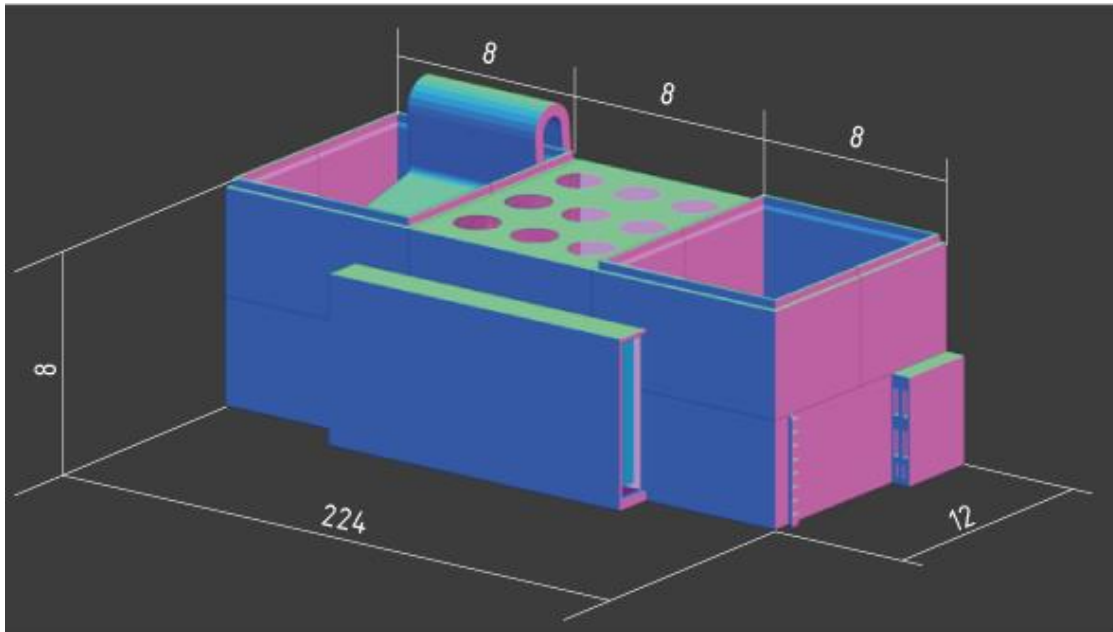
Diseño tridimensional del conjunto dimensionado
